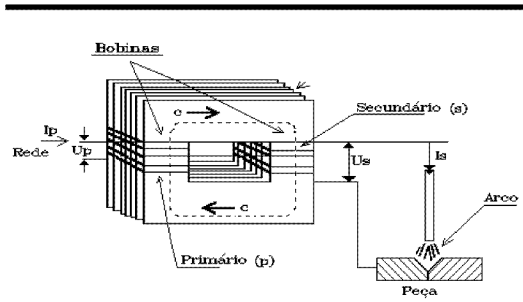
Elementos Básicos de um Transformador para Soldagem.
